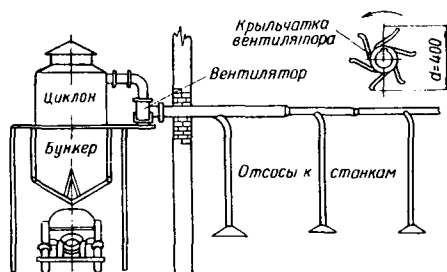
Принципиальная схема пневматической установки для уборки стружки и древесных отходов.
